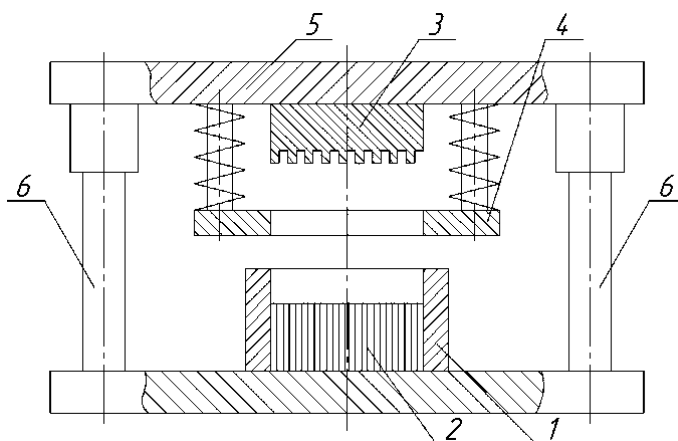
Схема приспособления для торцевого прессования прямоугольных шипов в древесине: 1 – зажимной элемент; 2 – заготовка; 3 – пуансон; 4 – подвижный съемник; 5 – верхняя плита; 6 – колонки
